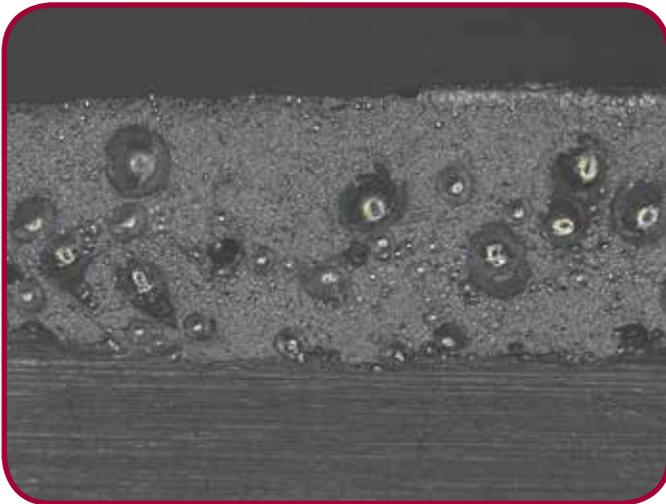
Porosidad dispersa que se encuentra en la estructura interna de una soldadura de aluminio después de una prueba de rotura por flexión con entalladura.
